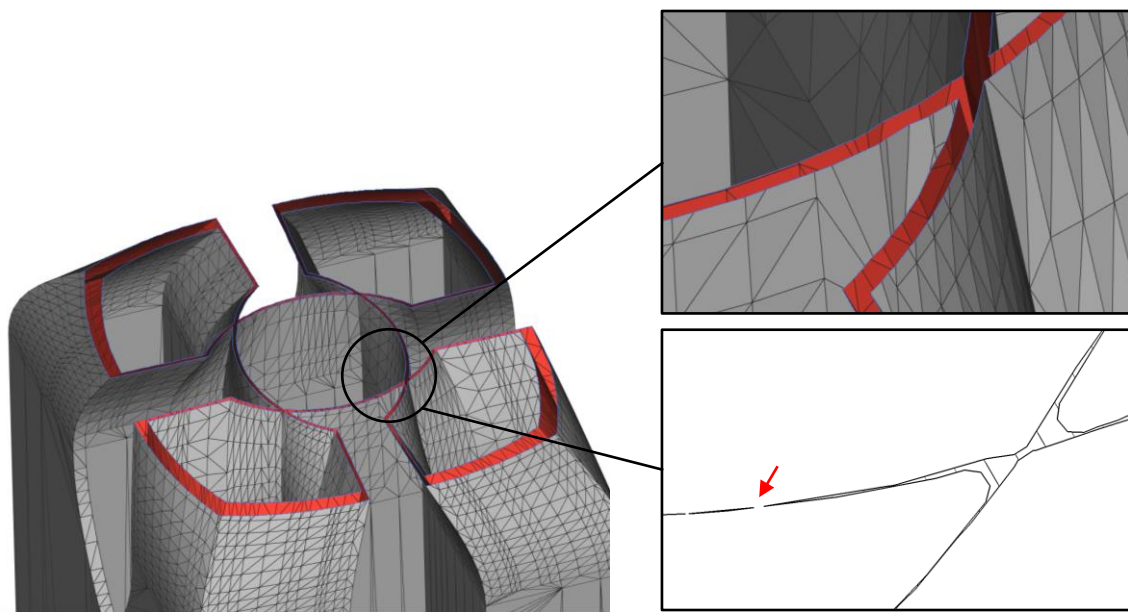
Defekty jednotné skenovací dráhy v náhodných řezech součásti
